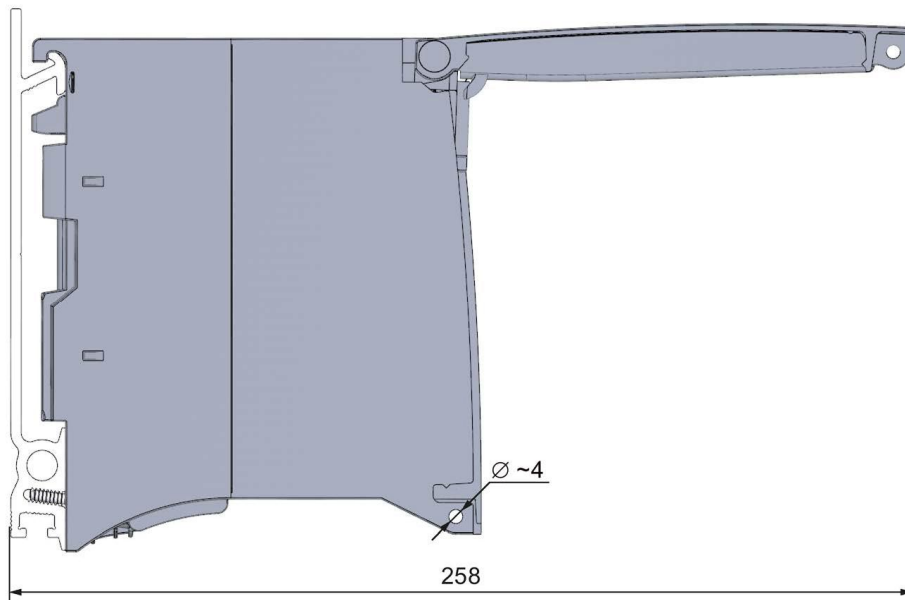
Габаритный чертеж CPU 1518-4 PN/DP, (вид сбоку, открытой передней крышкой)
